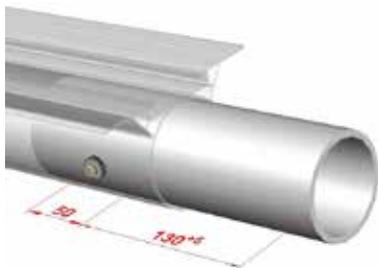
Einstecken und verschrauben des Stoßprofils
